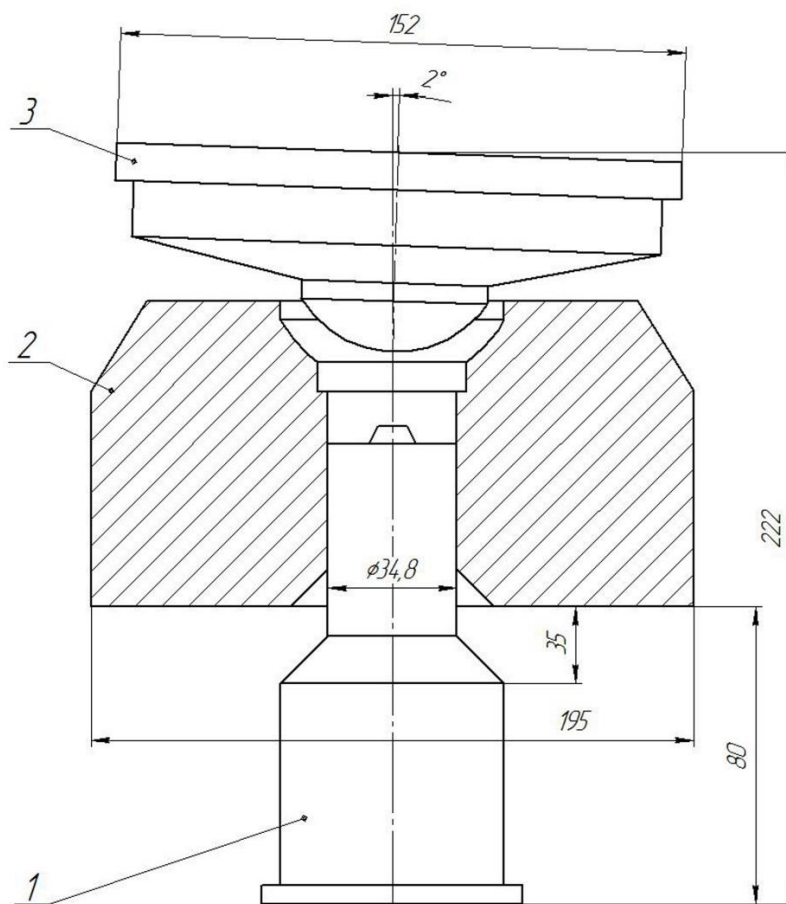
Эскиз заготовки детали «Стакан», полученной штамповкой в холодном состоянии на сферодвижном прессователе
